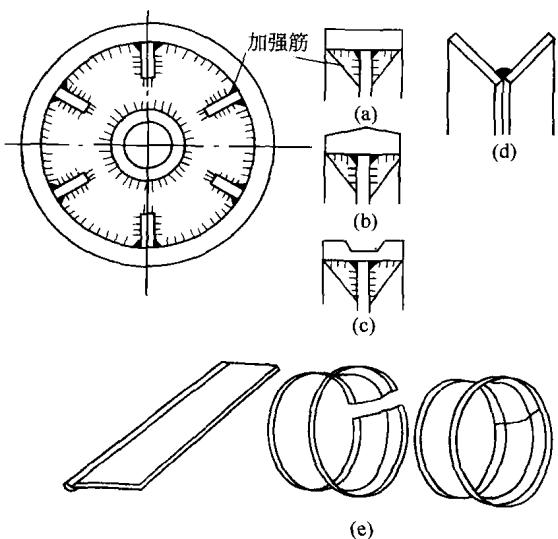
圆盘形焊接零件的轮缘结构
